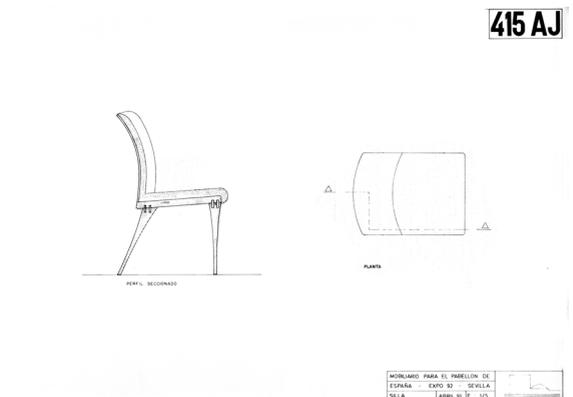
Hoja de planimetría de la silla. Arxiu Valencià del Disseny, 2018.
